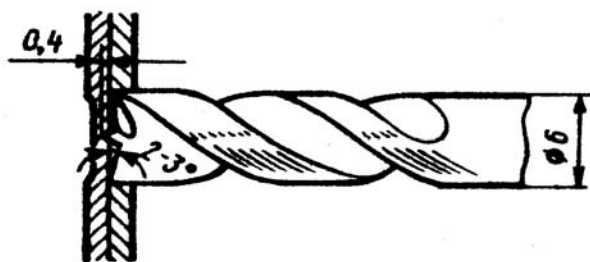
Непосредственное зенкование точки сварки специально заточенным сверлом по типу фрезы
